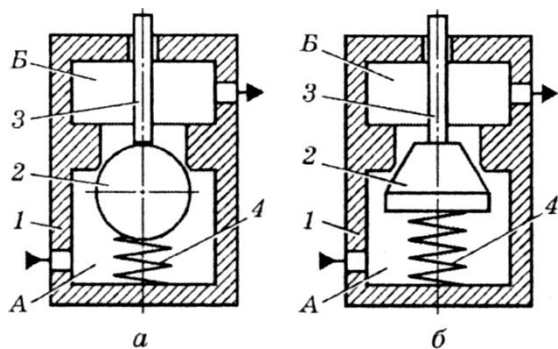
Схеми клапанних розподільників: *a* – кулькового; *б* – конічного; 1 – корпус; 2 – запірно-регулювальний елемент; 3 – штовхач; 4 – пружина; *A* – напірна порожнина; *B* – робоча порожнина
